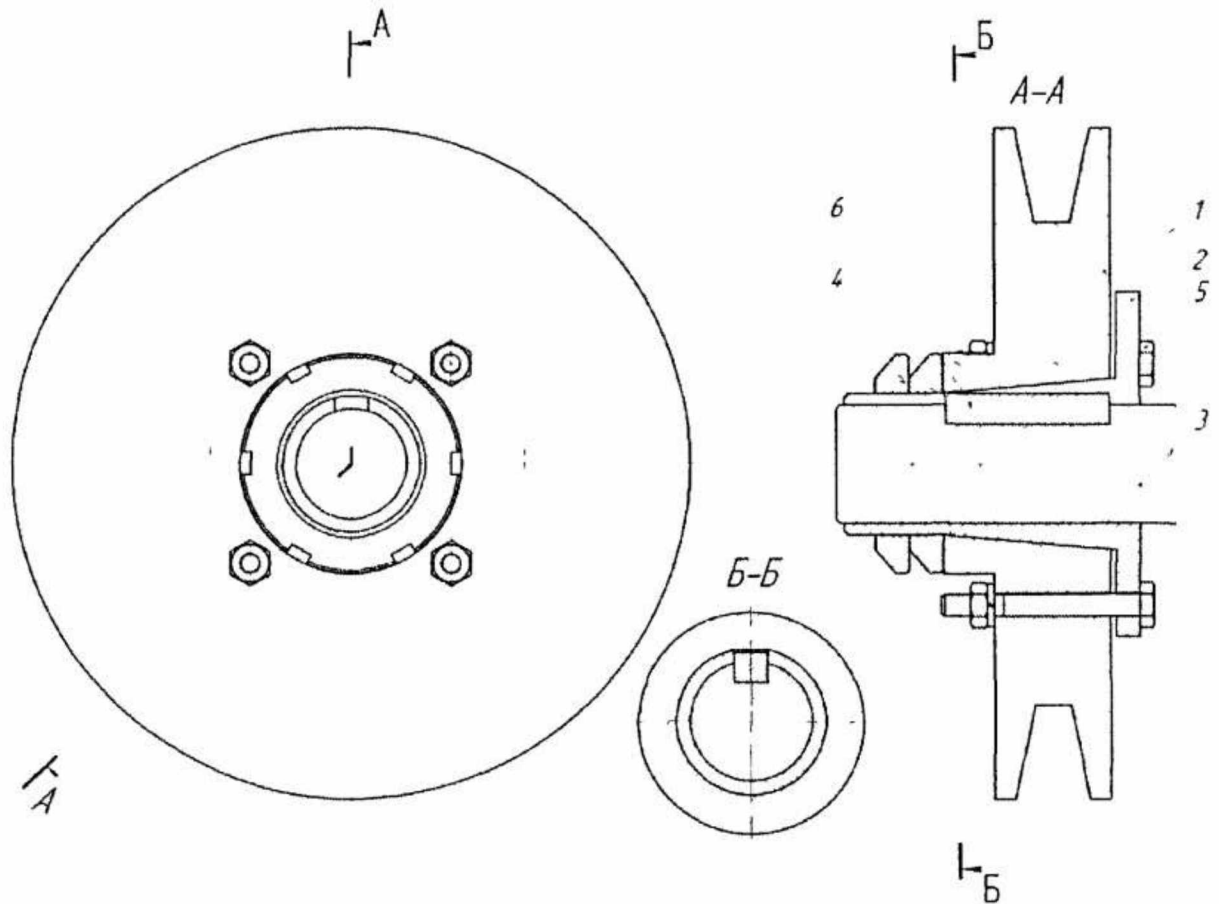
Спосіб з'єднання з натягом деталей вал-втулка
